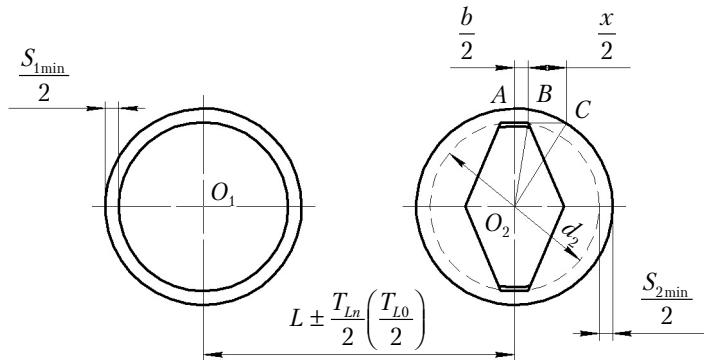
Расчетная схема при установке заготовки на срезанный и цилиндрический пальцы
